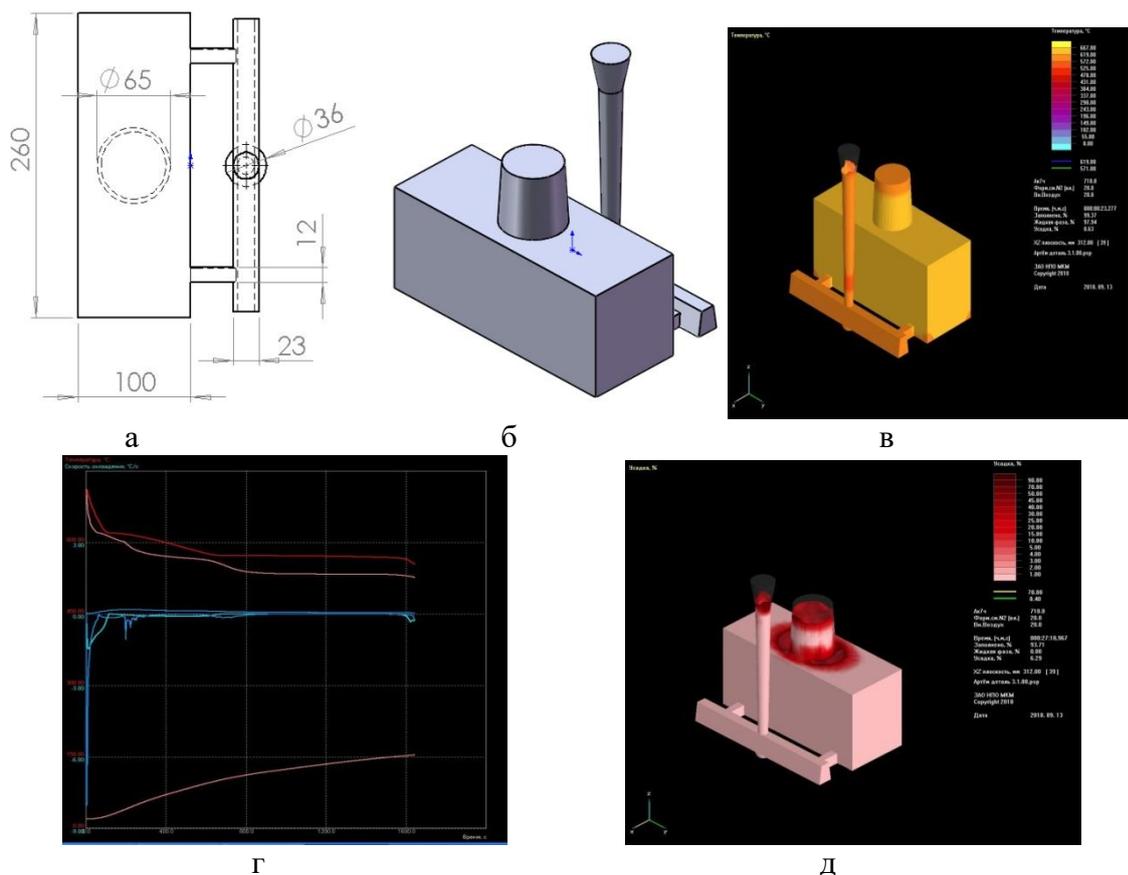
Моделирование отливки: а - технологический чертеж, б - 3D модель отливки с прибылью, в – температурные поля отливки, г- скорость охлаждения отливки, д - усадка отливки.
